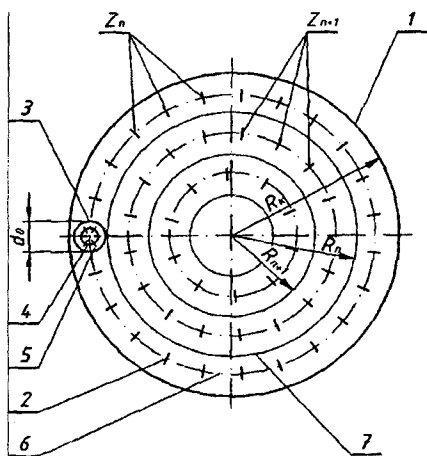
Принципиальная схема новой конструкции матрицы: 1 – корпус; 2 – колодцы; 3 – вкладыши; 4 – отверстия формующие; 5 – гнездо; 6 – центральный радиус условного кольца; 7 – кольцо условное
